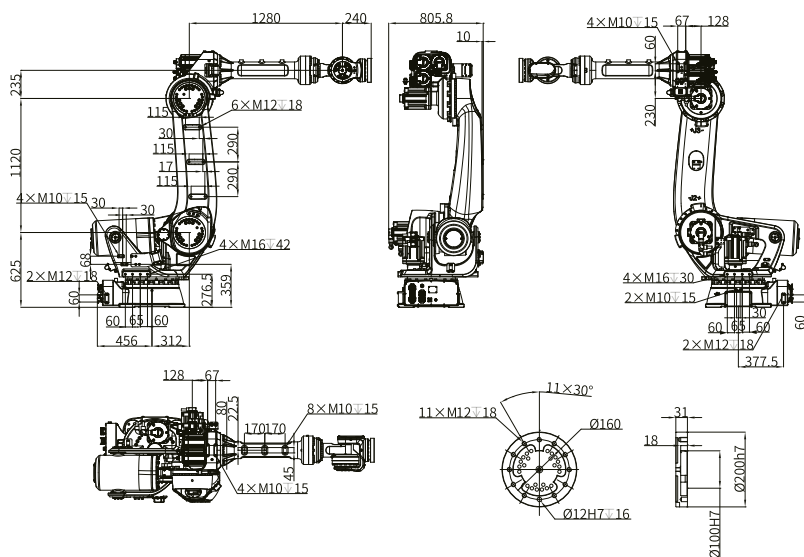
Габаритные размеры робота IR-R220/IR-R170
